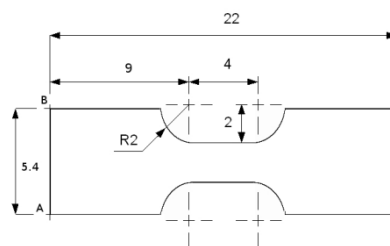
Dimension des éprouvettes pour la micromachine de traction sous binoculaire.
